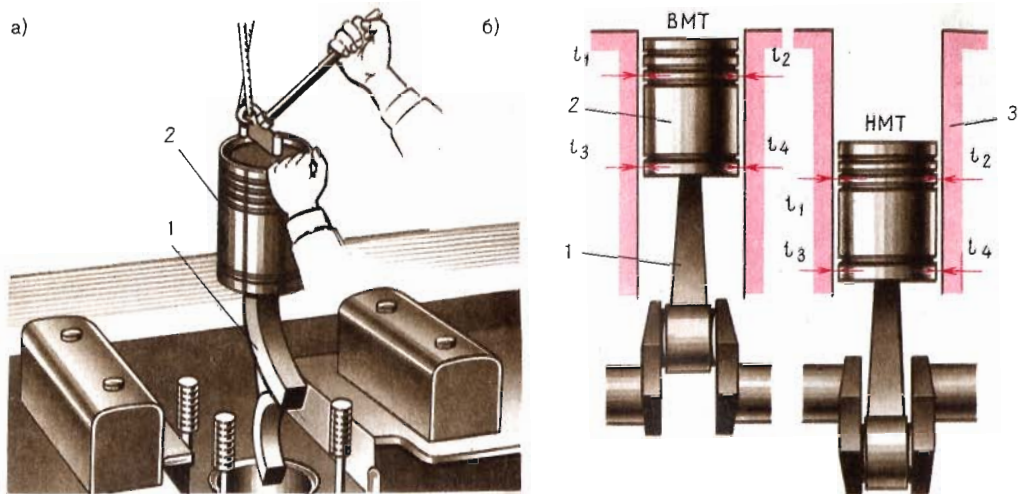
Измерение зазора между поршнем и втулкой цилиндра
